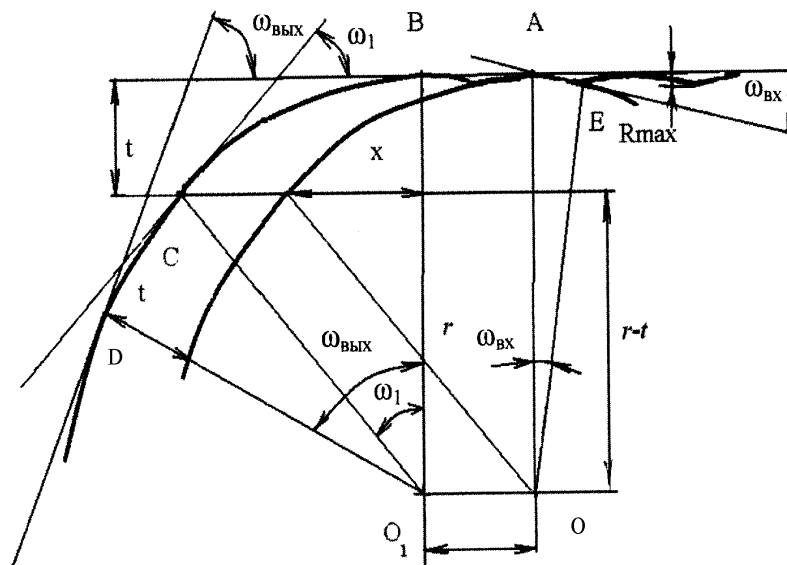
Схема для расчета положения изношенных участков при точении резцом, оснащенным пластиной ПКНБ круглой формы
